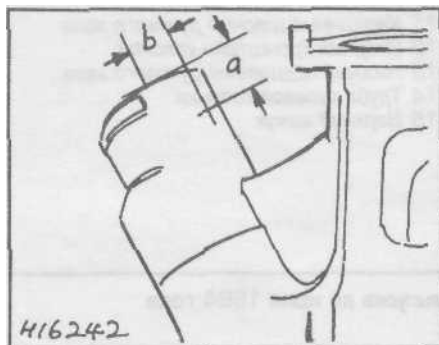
Место для сверления при снятии цилиндра рулевой колонки
